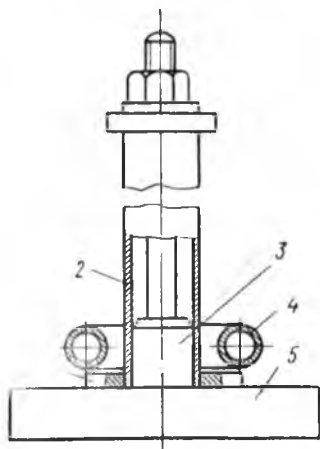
Приспособление для индукционной пайки фланца с волноводом:
